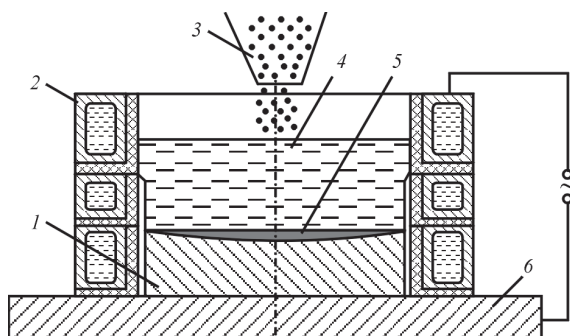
Схема наплавки штампов в ТПК с использованием дискретной присадки в виде стружки: 1 — наплавляемый штамп; 2 — токоподводящий кристаллизатор; 3 — присадка (стружка); 4 — шлаковая ванна; 5 — металлическая ванна (наплавляемый металл); 6 — поддон
